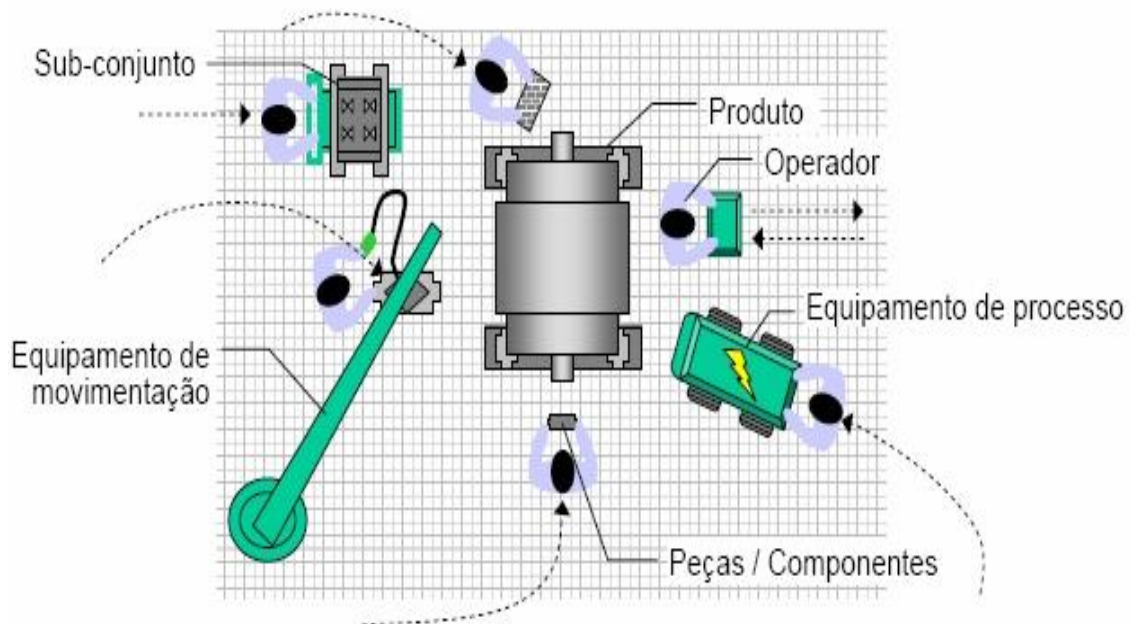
Arranjo Físico Posicional ou de Posição Fixa.
